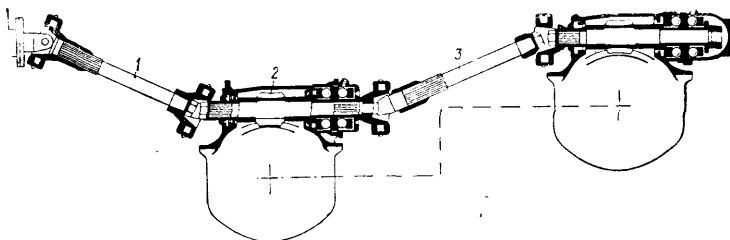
Схема передачи по типу FWD. 1—карданный вал от коробки передач; 2—проходной червяк; 3—второй карданный вал.
